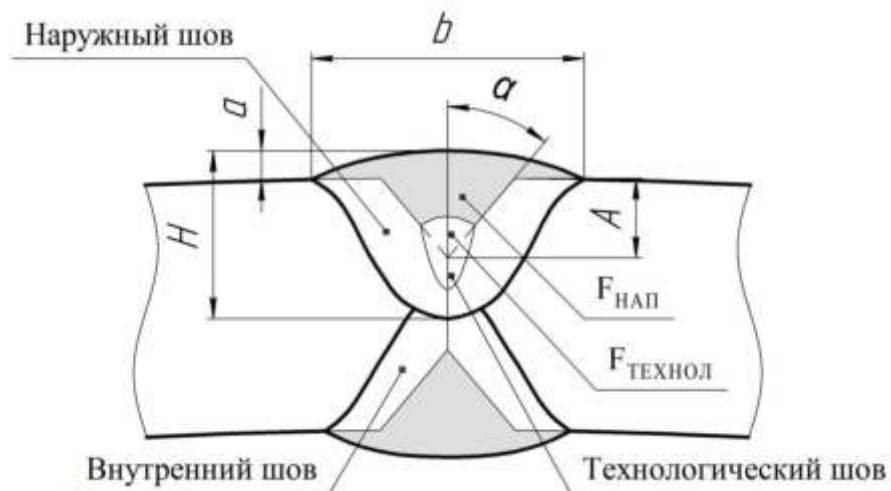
Схема продольного сварного соединения трубы
